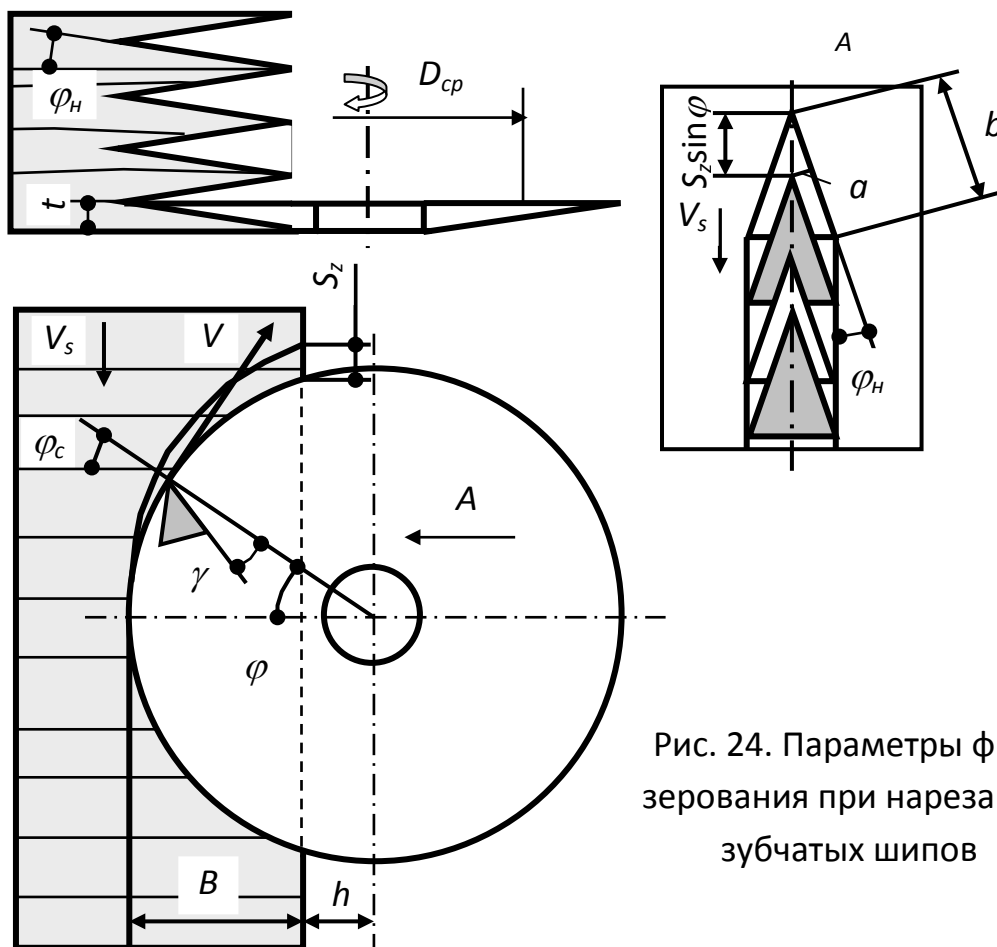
Параметры фрезерования при нарезании зубчатых шипов
